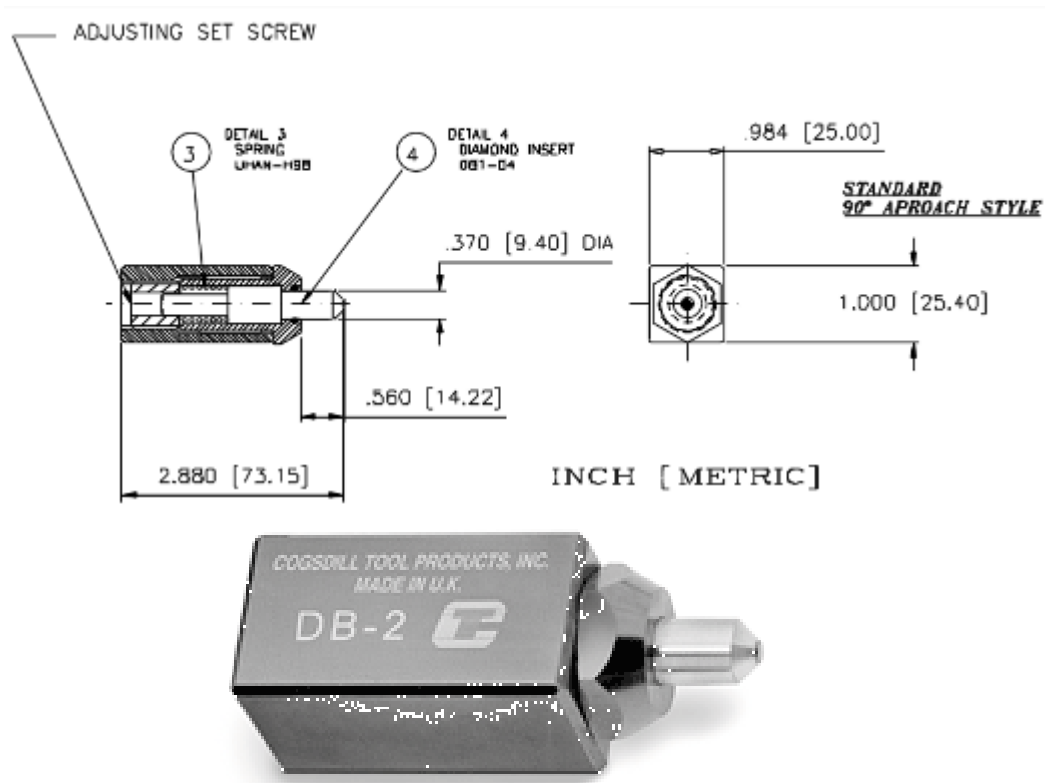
Инструмент DB-2 Cogsidill Tool
